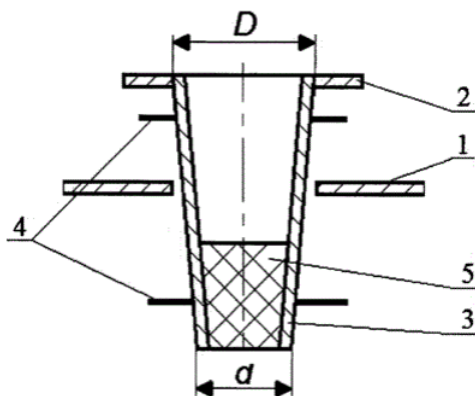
Схема конструкции клапана поропластовой тарелки [6]:
